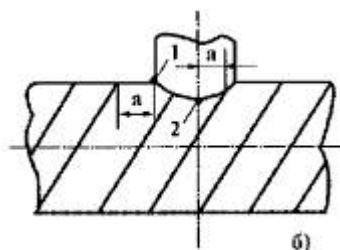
Сварка патрубков (штуцеров) с трубопроводами со спиральными швами: спиральный шов допускается;
